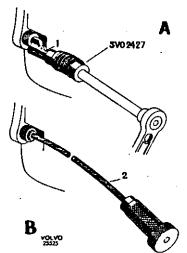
Ausbau der Getriebeschrauben, Wagen mit B 16-Motoren
